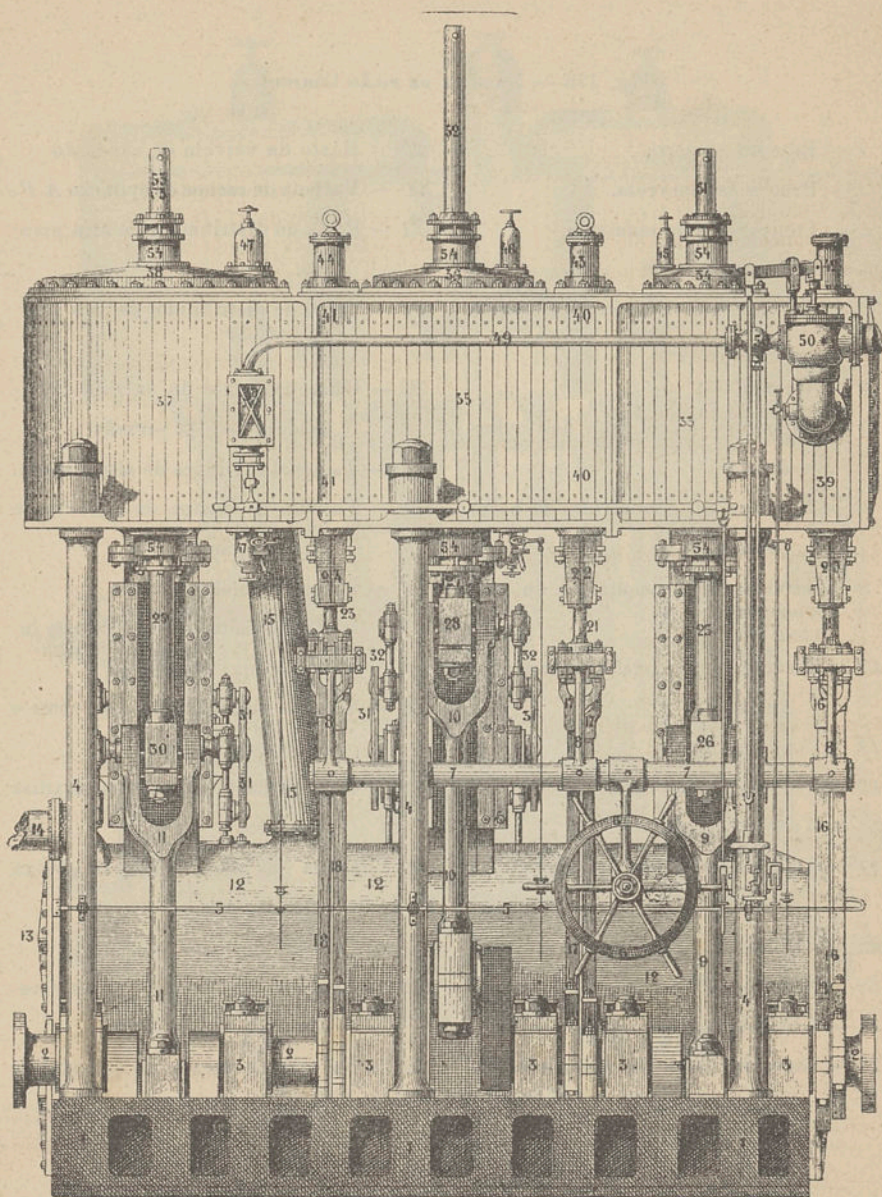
MACHINA DE PILÃO DE TRIPLICE EXPANSÃO
